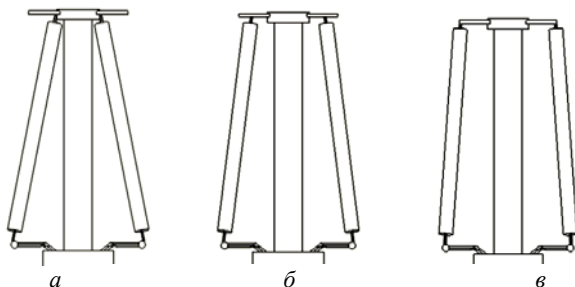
Расположение контактов СИЭ в верхней части опорной конструкции:
